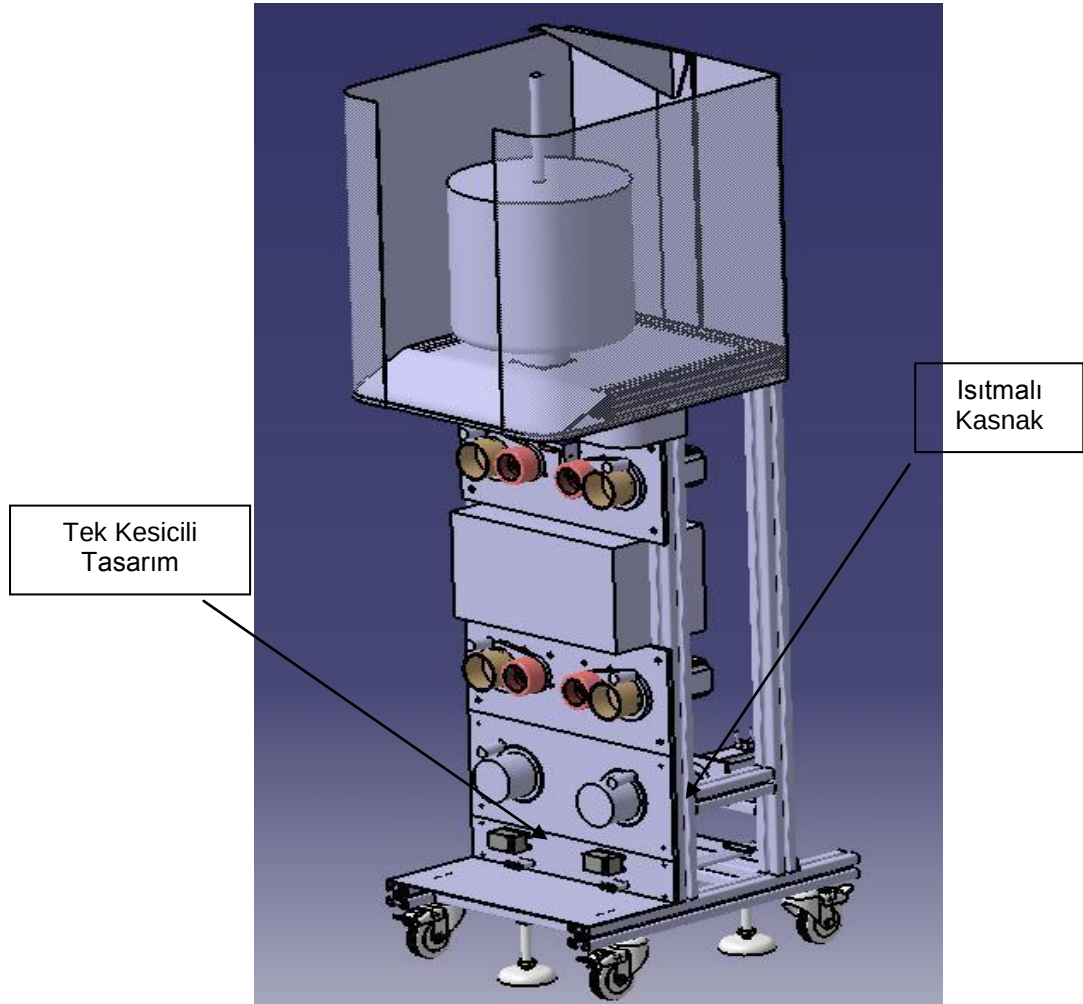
İlk Kesici Yerleşimi Planı
